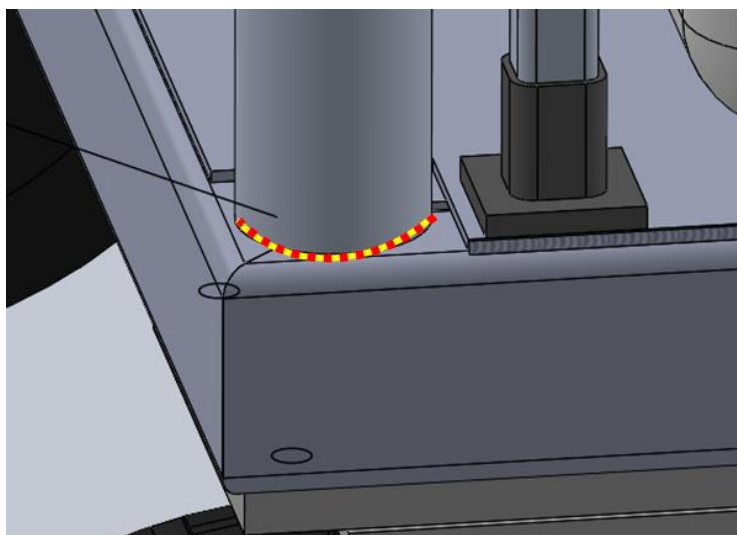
Representación de la soldadura de la unión EMPUJE-CHASIS [fuente propia]
